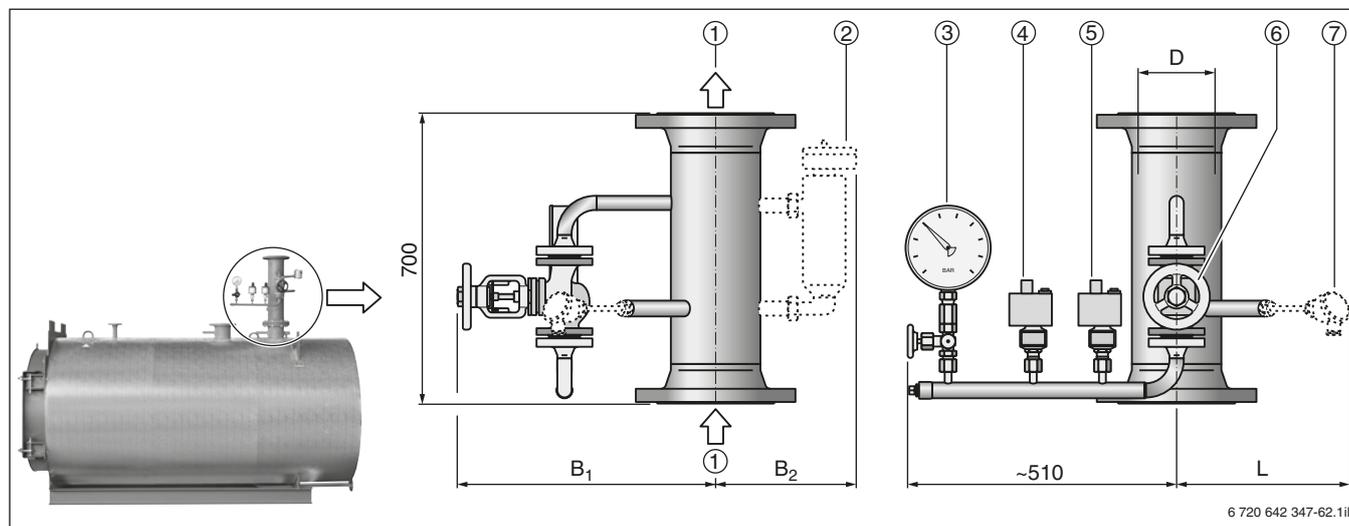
Conjunto de equipo de seguridad de la caldera para las calderas UNIMAT UT-L (pieza de impulsión intermedia con conjunto de seguridad y válvulas de la caldera; dimensiones en mm)
